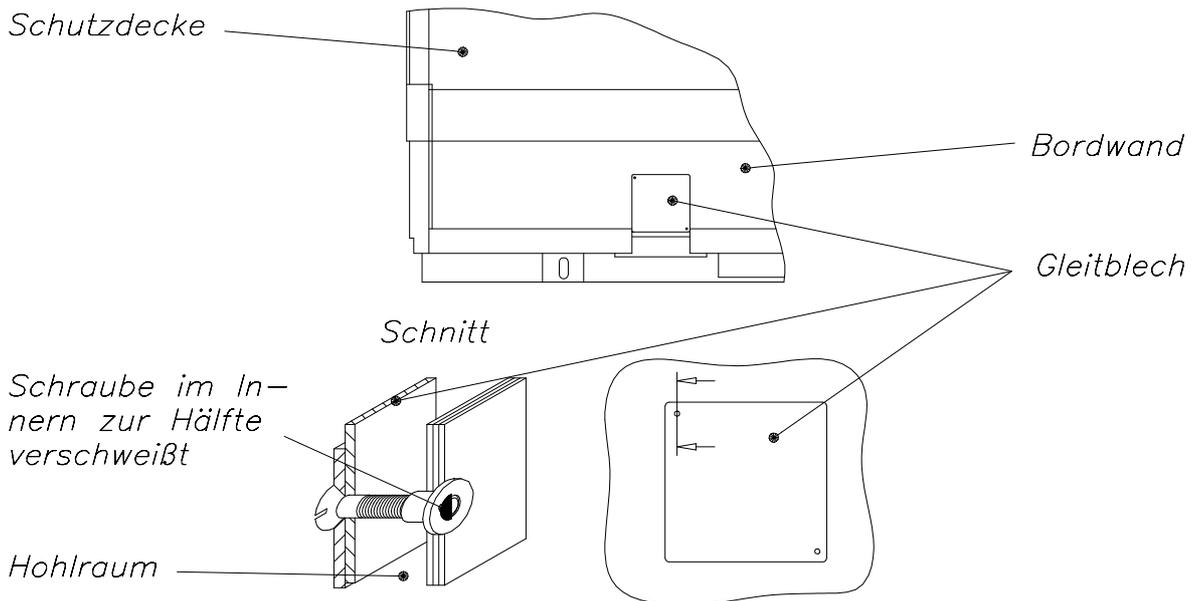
Befestigungsvorschlag für Gleitbleche bei Hohlprofilen
